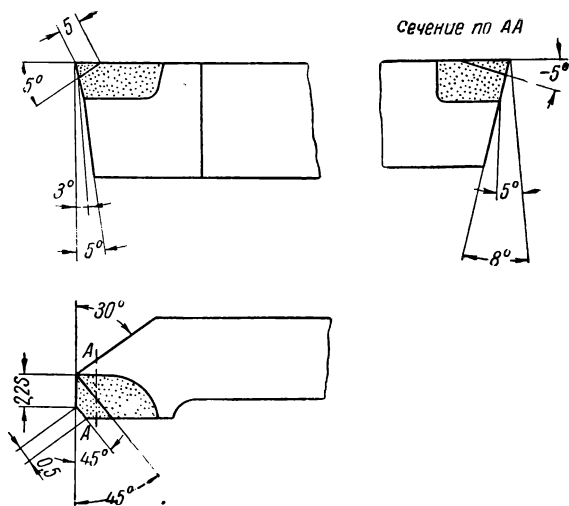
Левый проходной резец для точения с большими подачами конструкции К. В. Лакура.
